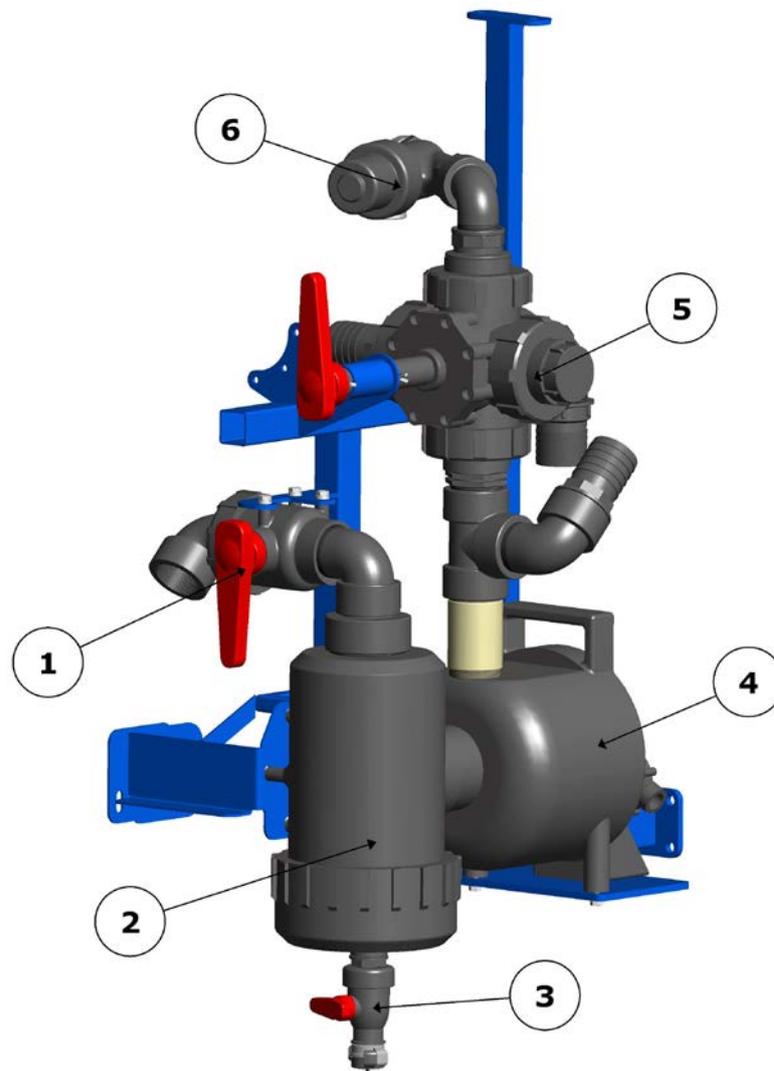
/3 Beschreibung der Steuerelemente Variante SAUGEN-FILTER 3“-BEFÜLLPUMPE
